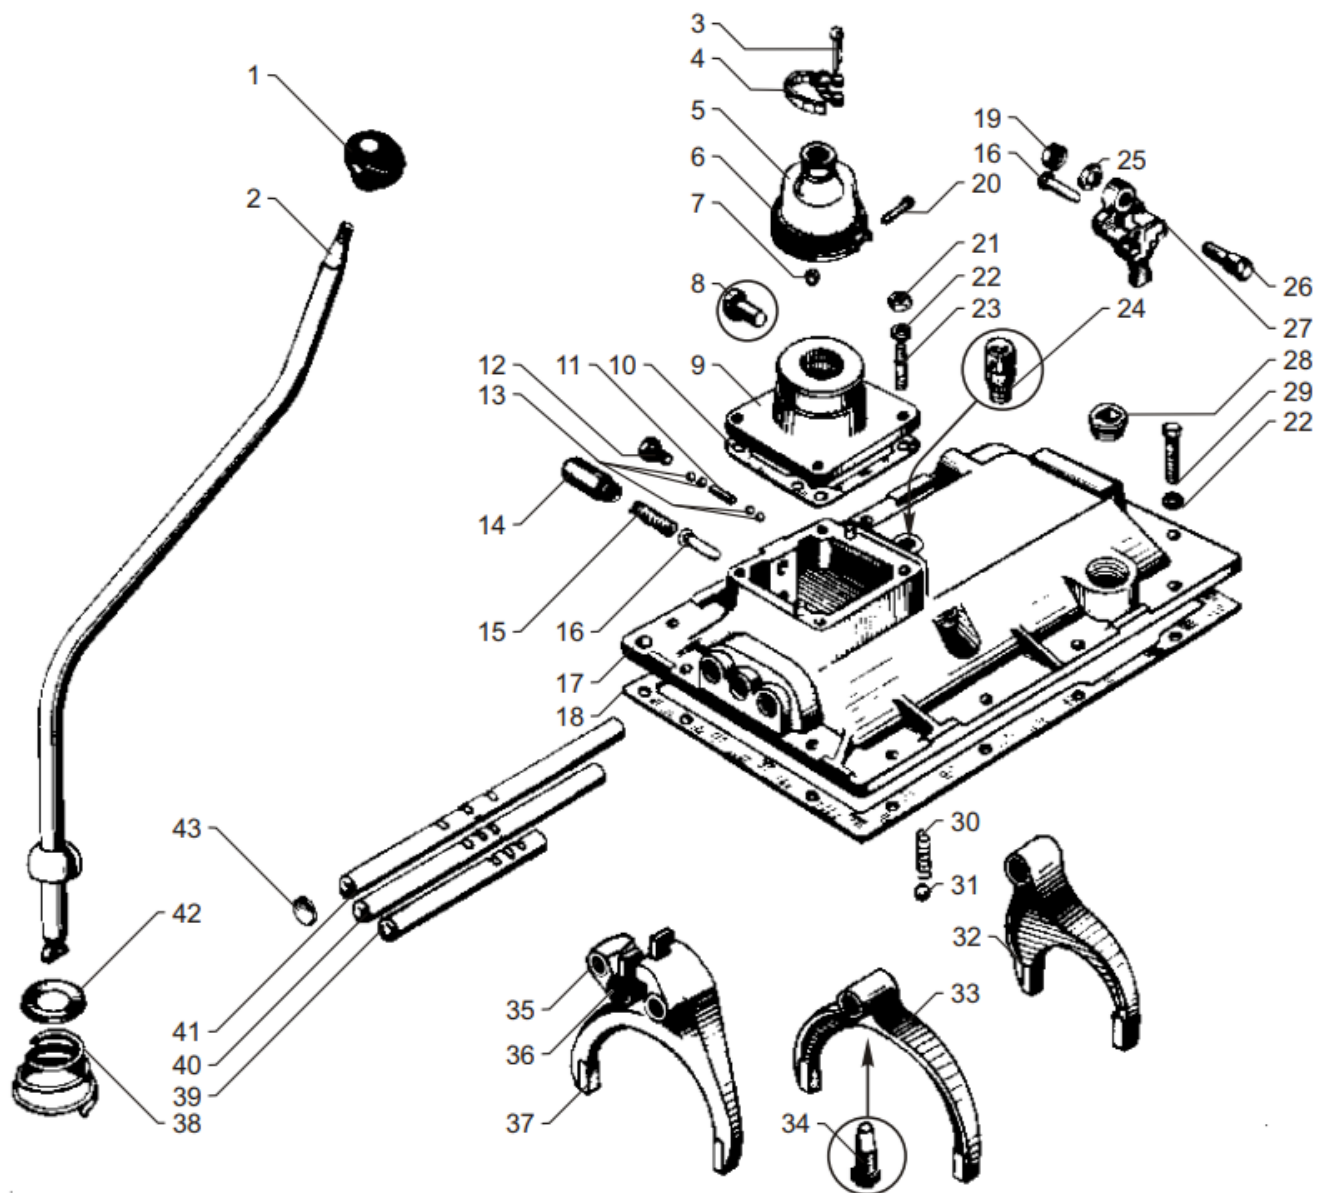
МЕХАНИЗМ ПЕРЕКЛЮЧЕНИЯ ПЕРЕДАЧ КОРОБКИ ПЕРЕДАЧ ЯМЗ-236Н
